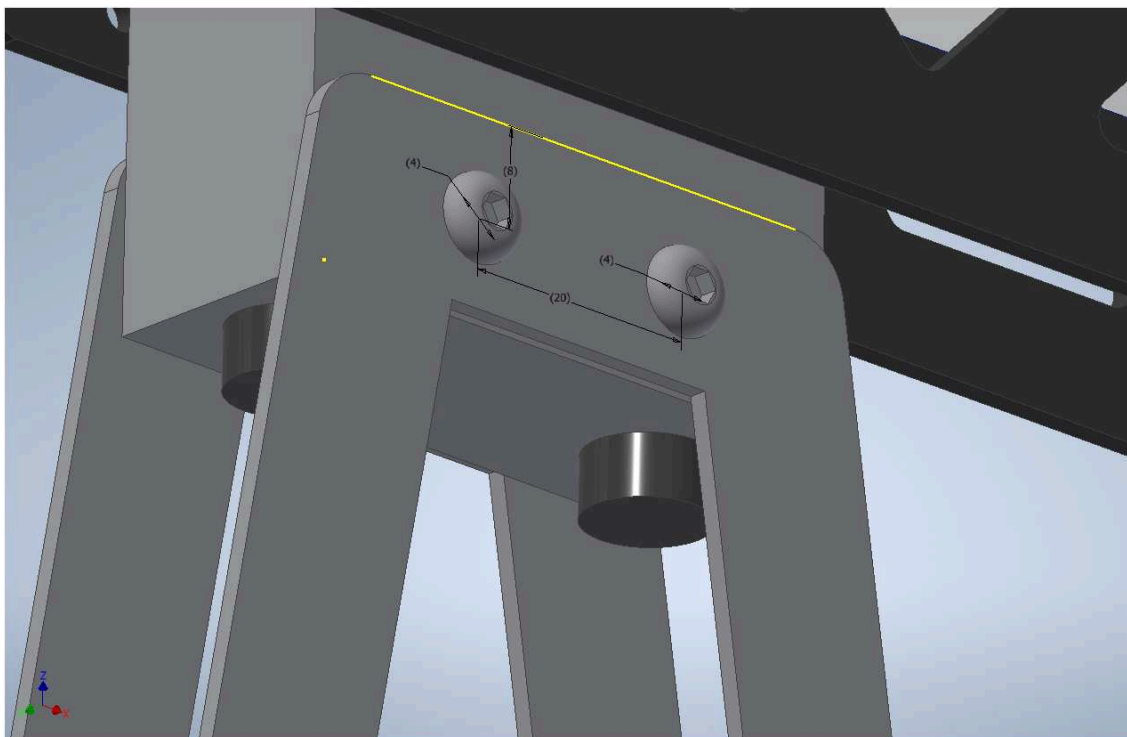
Схема закрепления пластин к рейке крепления полезной нагрузки.
